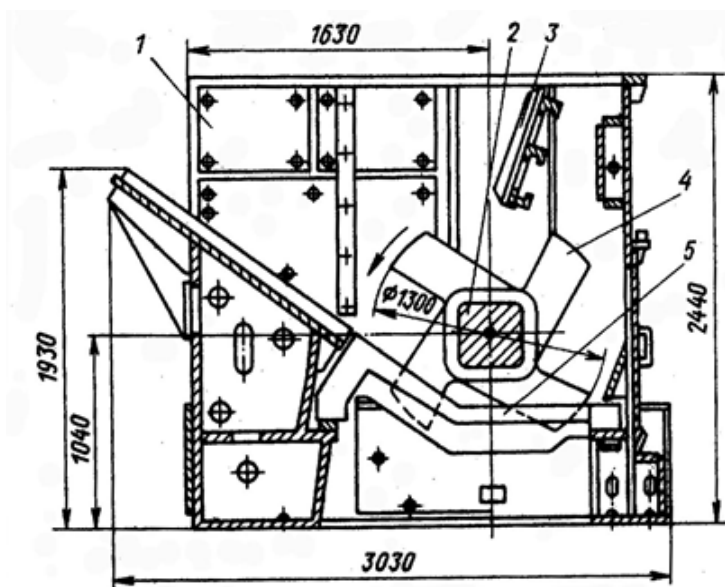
Конструкция одновалковой зубчатой дробилки завода «Электросталь»
